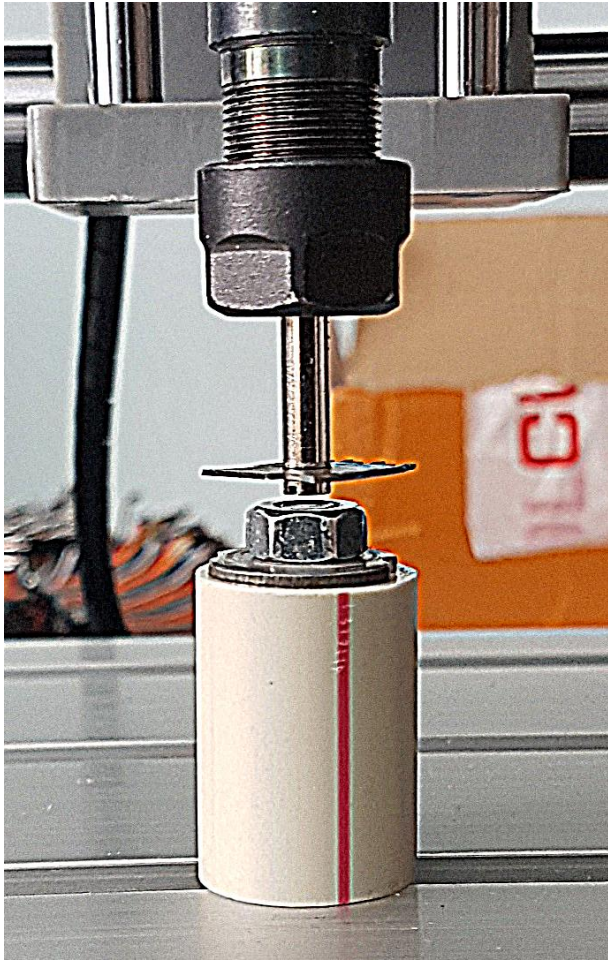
Заготовка, закріплена на верстаті CNC 3018 Pro
